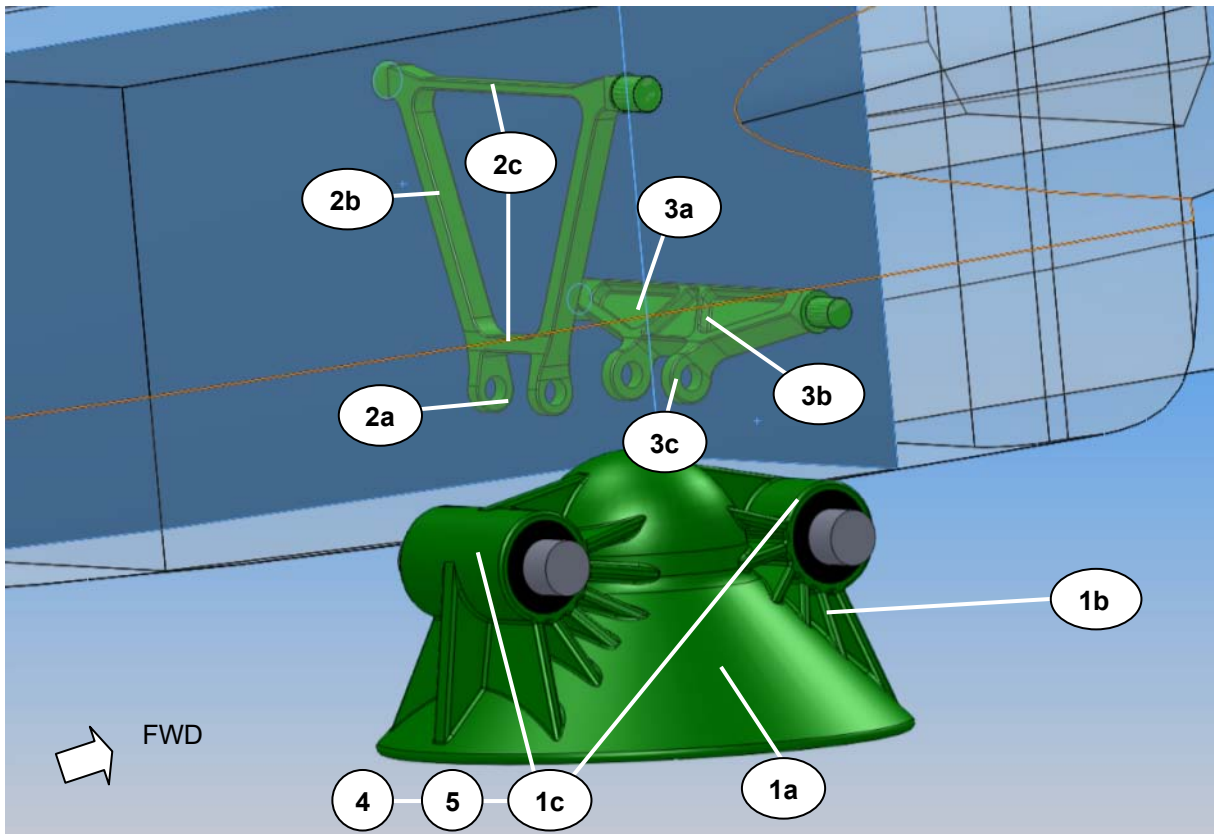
Aufbau der Baugruppe Schnittstelle Rumpffahrwerk
